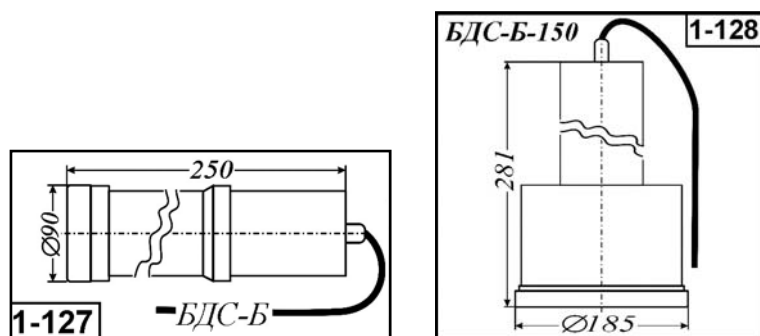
Внешний вид и габаритные размеры блоков детектирования БДС-Б и БДС-Б-150
